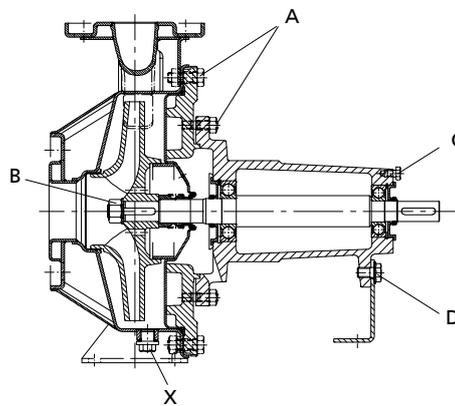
Позиции затяжки винтов диаметр рабочего колеса 250, 50-200, 65-200, 80-200
